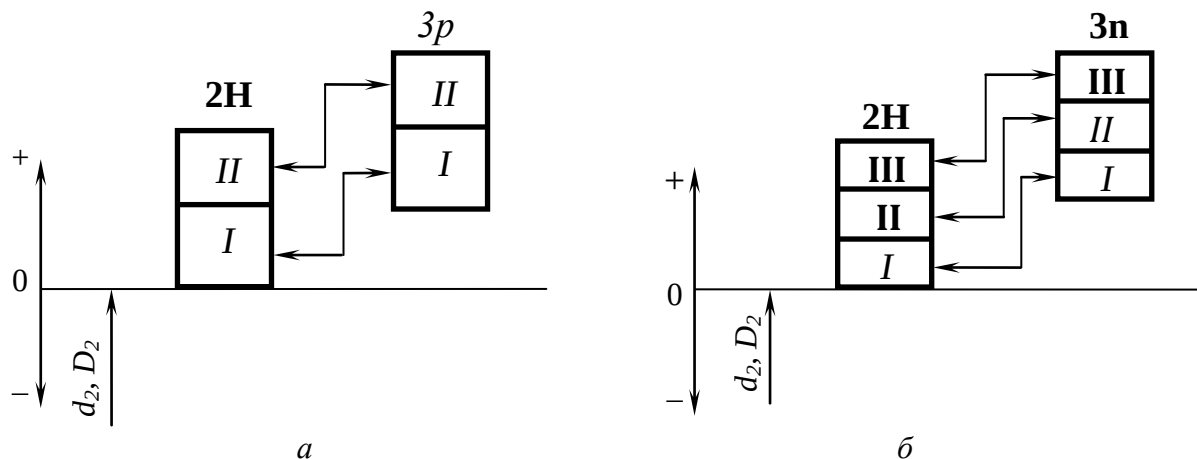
Схемы полей допусков резьбы с сортировкой:
